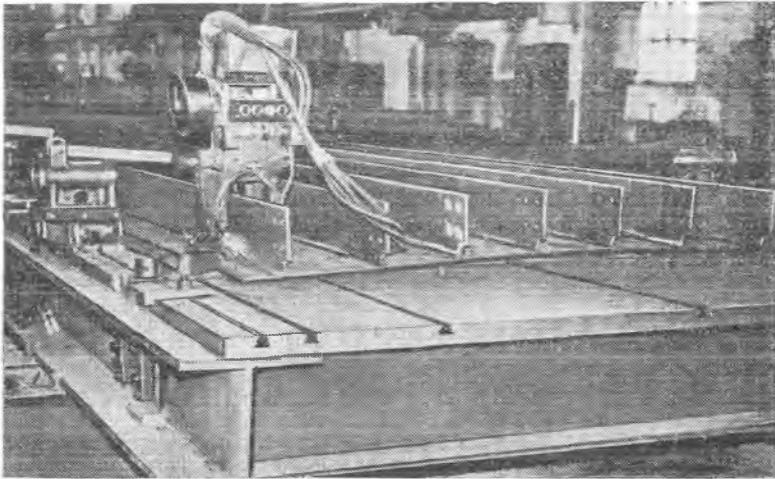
Сборочно-сварочный кондуктор для изготовления ортостропных плит
